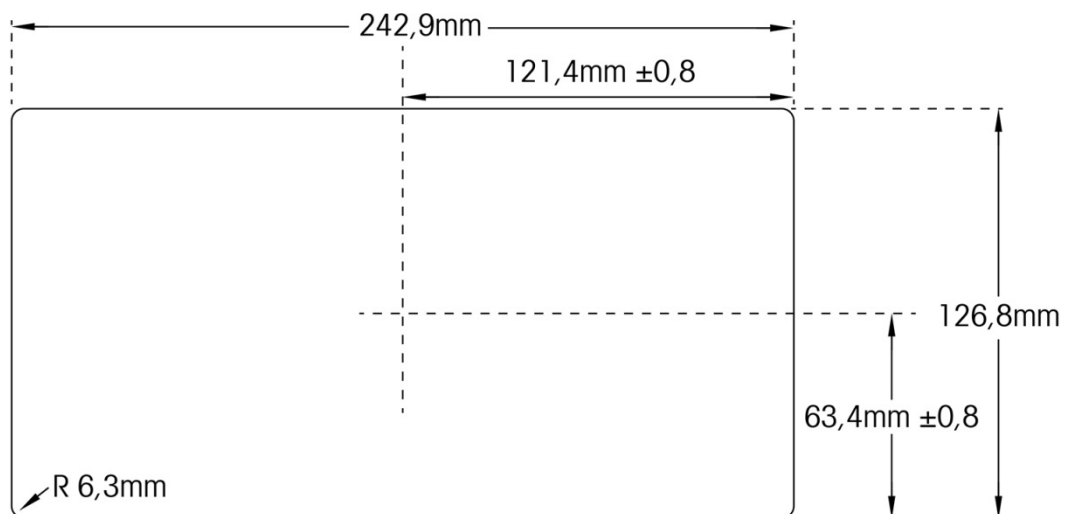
Dimensões do Gabinete do IND570 em Corte para Montagem em Painel
